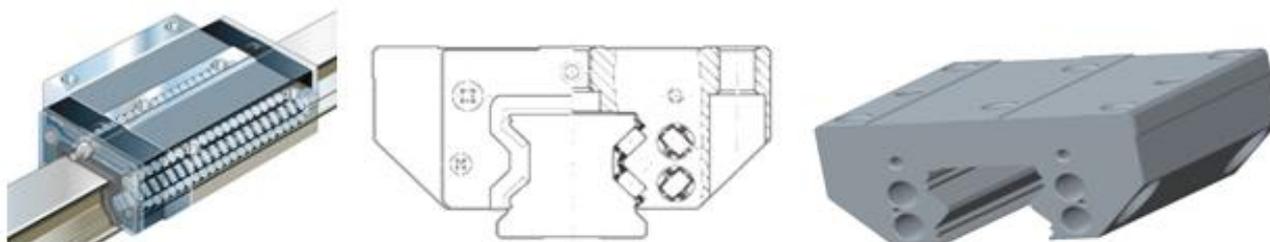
Rollenwagen mit Rücklaufbohrungen
